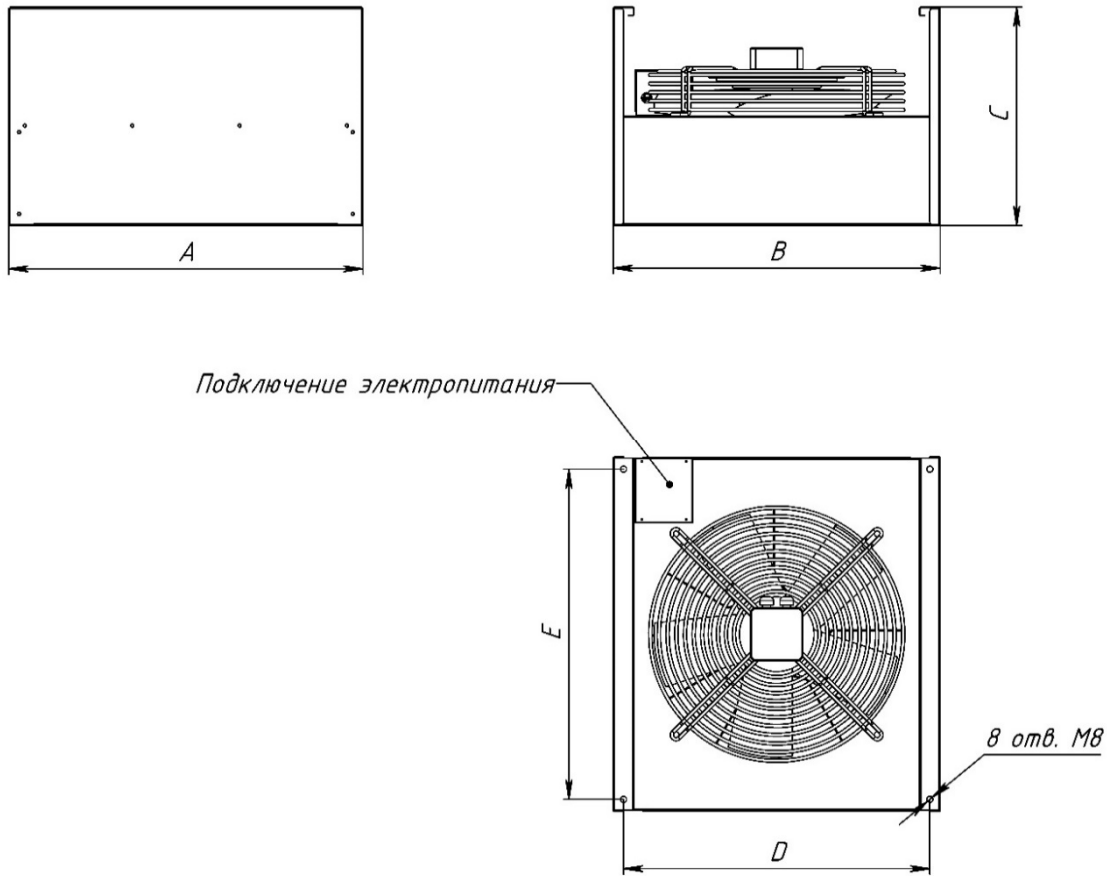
Габаритные и присоединительные размеры SA1 3600/5500 D
